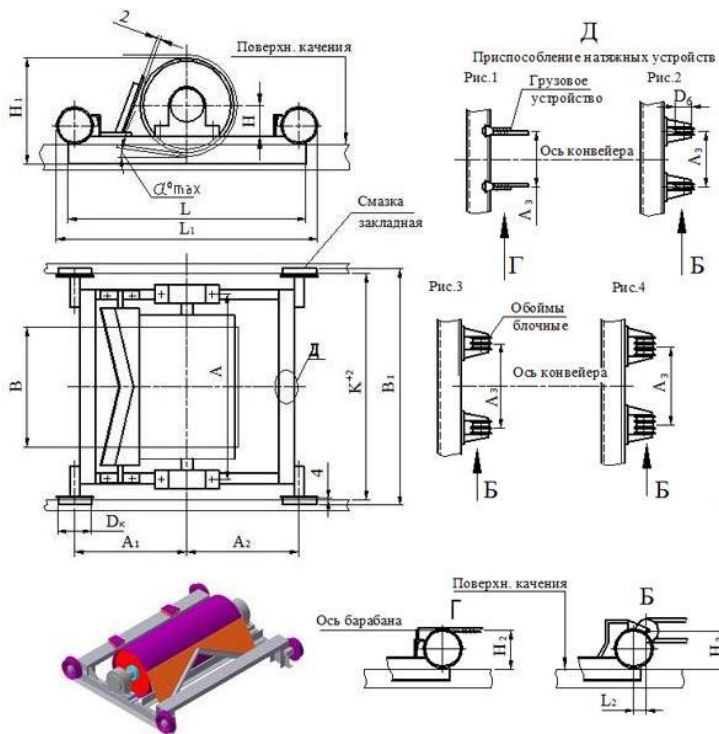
Загальний вид натяжного візка з не футерованим барабаном
